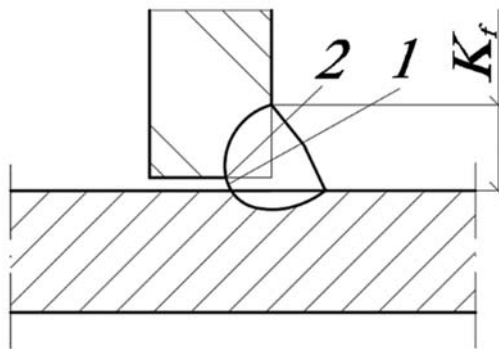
К расчету стыкового сварного шва на срез
